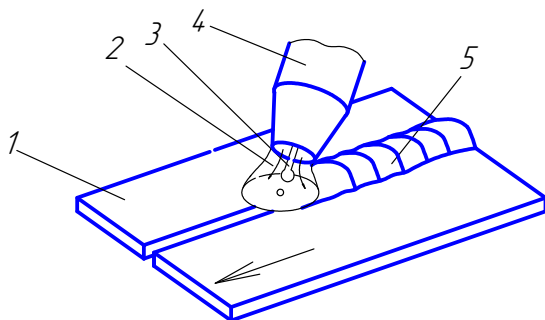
Схема сварки плавящимся электродом в защитных газах:
